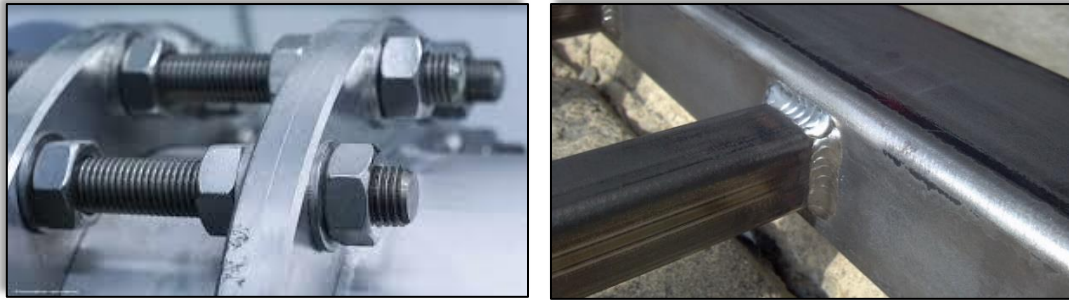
Unión atornillada (izq.) - Unión por soldadura (der.)
